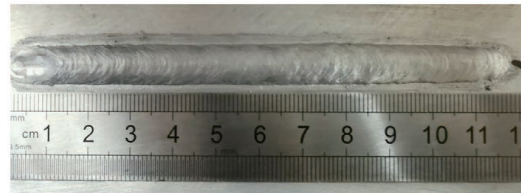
铝合金激光-MIG 复合焊缝的正面形貌
